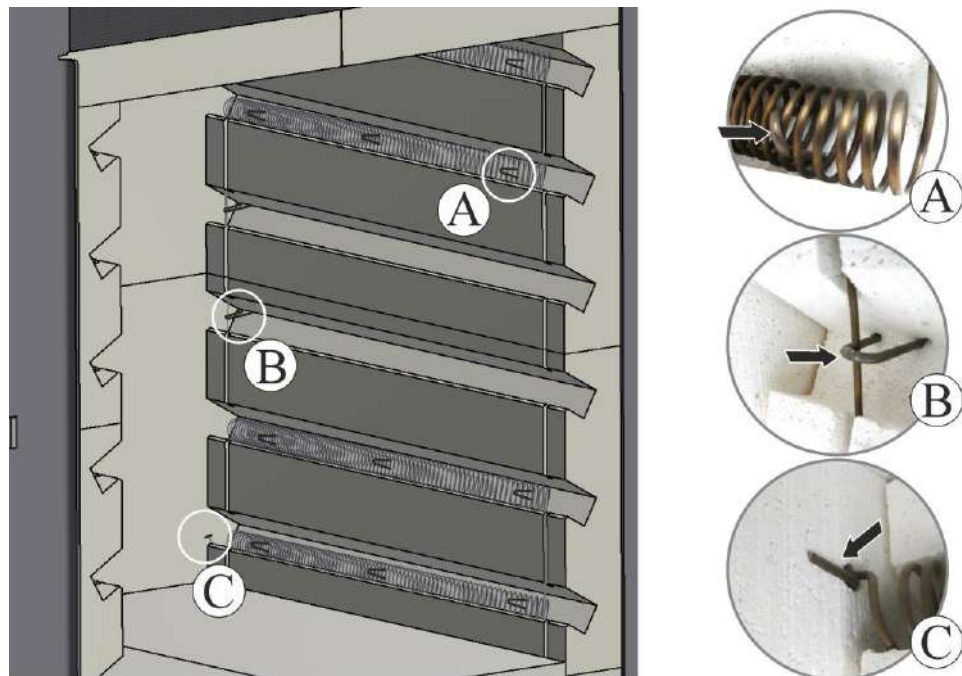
Așezați filamentul în canelura/canelurile și fixați cu capsă/capse (similar cu figura)
